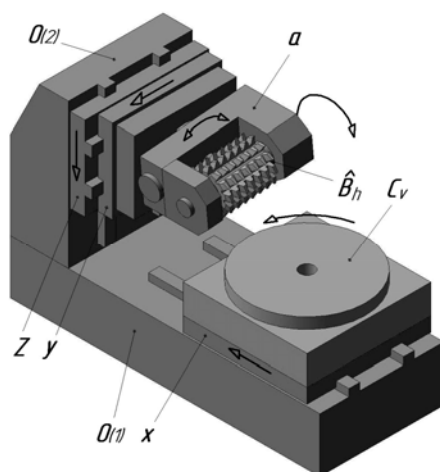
Компоновка зубофрезерного станка с формулой $CxOZYa\hat{B}$
